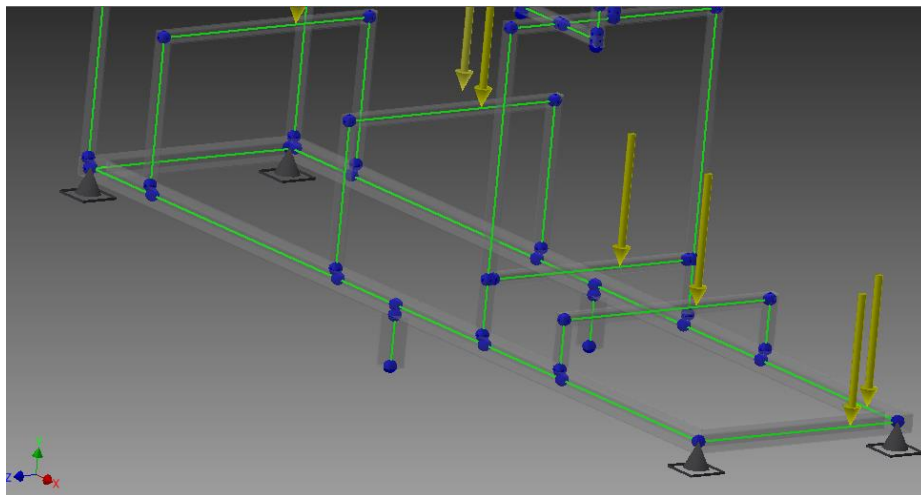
Apoyos en la estructura donde van ubicadas las ruedas de soporte. Fuente: Autor
